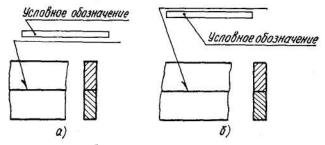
Нанесение условного обозначения шва сварного соединения, содержание и размеры граф таблицы швов не регламентируются
